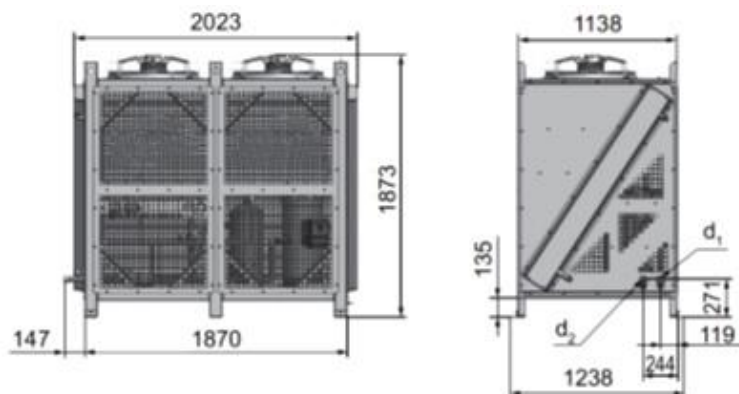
Загальний вид агрегату типу МАКК-120-621, МАКК-120-781
